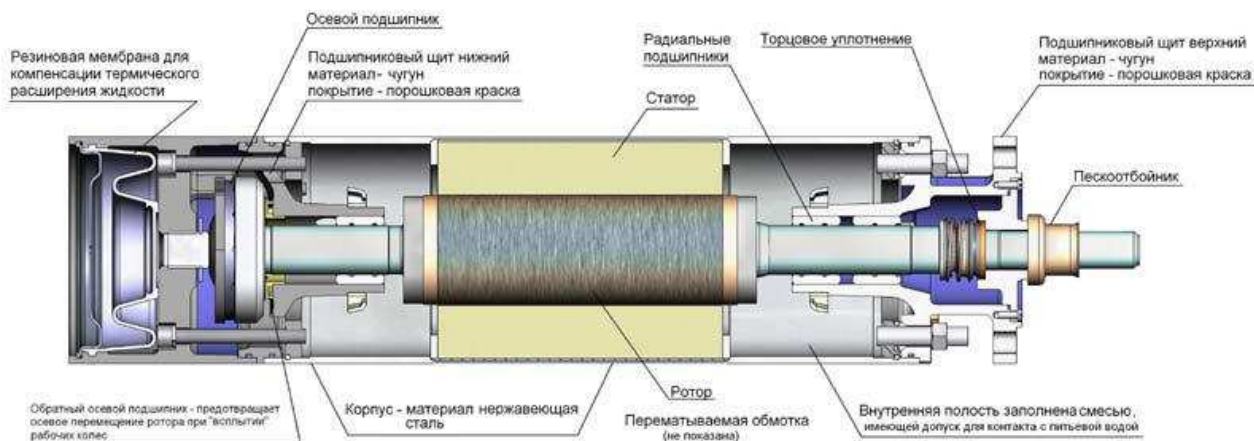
Конструктивная схема герметичного электродвигателя ДАП
